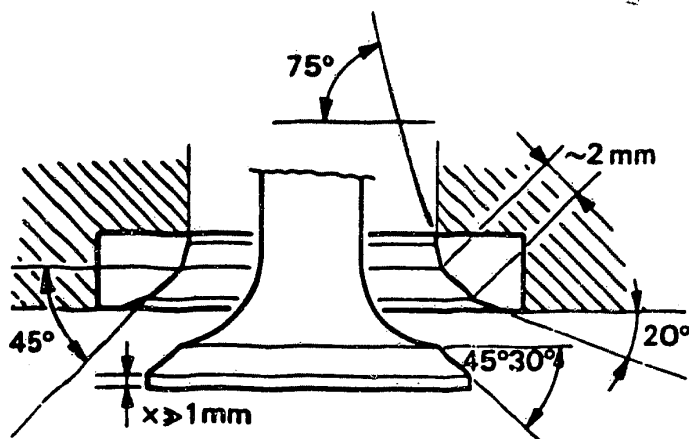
Die eingezeichneten Masse für die Bearbeitung der Ventile gelten bei allen drei Motoren sowohl für die Einlass- wie die Auslassventile.
